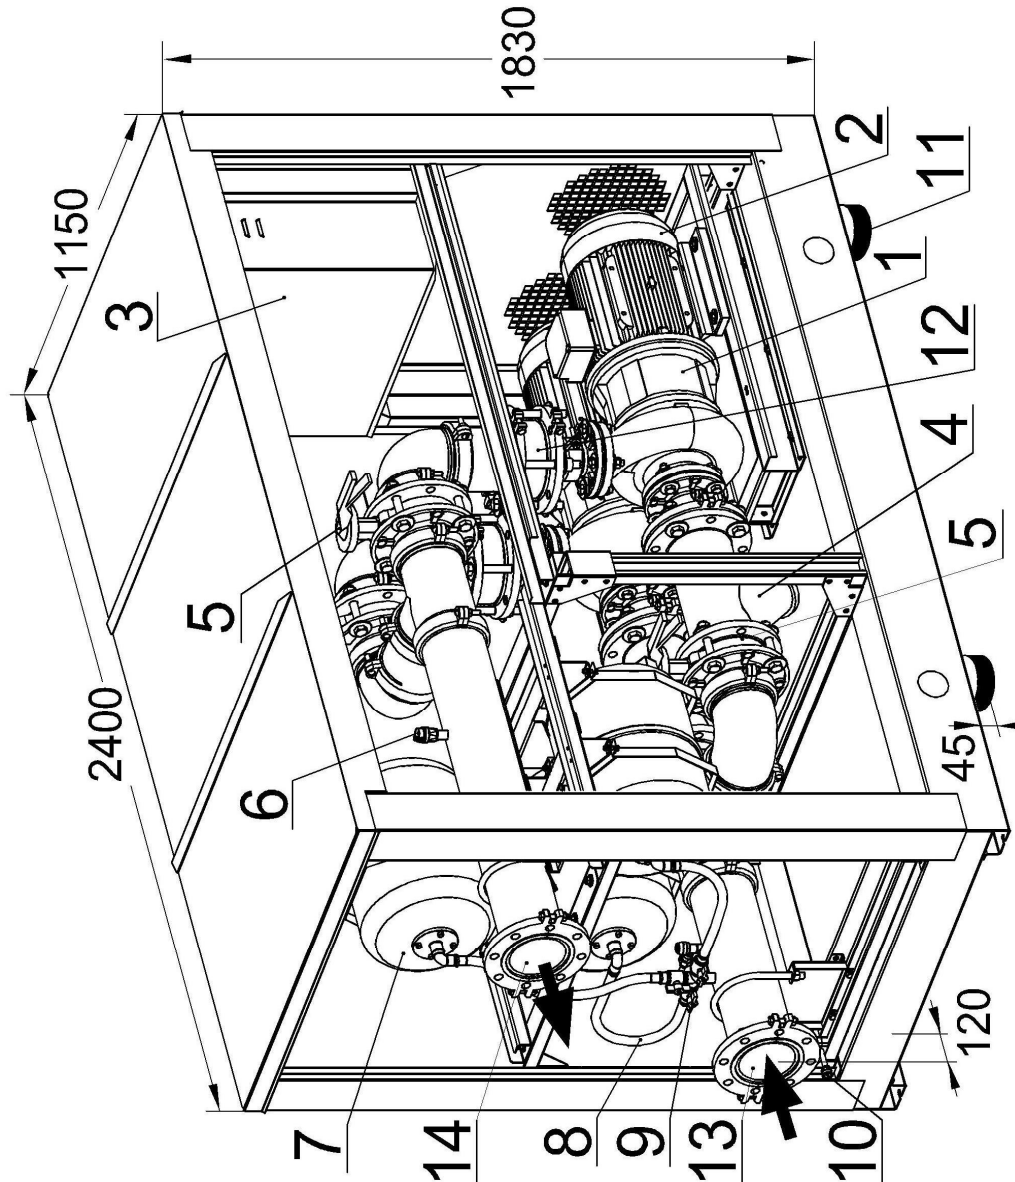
Компоновка и основные размеры агрегатов с двумя циркуляционными насосами
